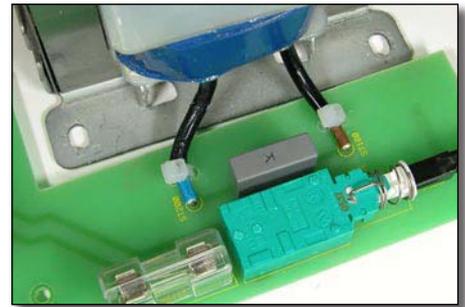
Die primärseitigen Anschlüsse des Netztrafos werden jeweils mit einem Isolierschlauch bestückt und mit einem Kabelbinder zusätzlich gesichert
